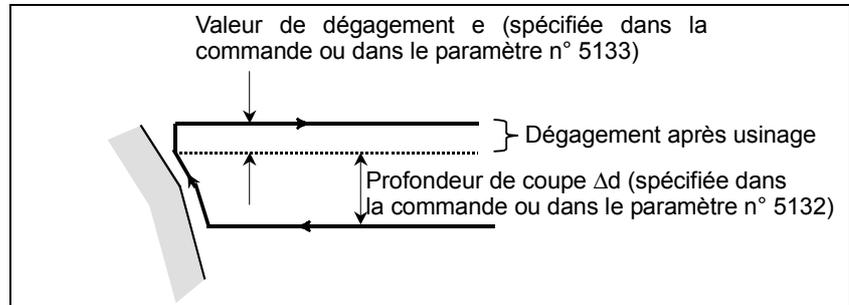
(j) Usinage suivant le profil de la pièce (type II)
